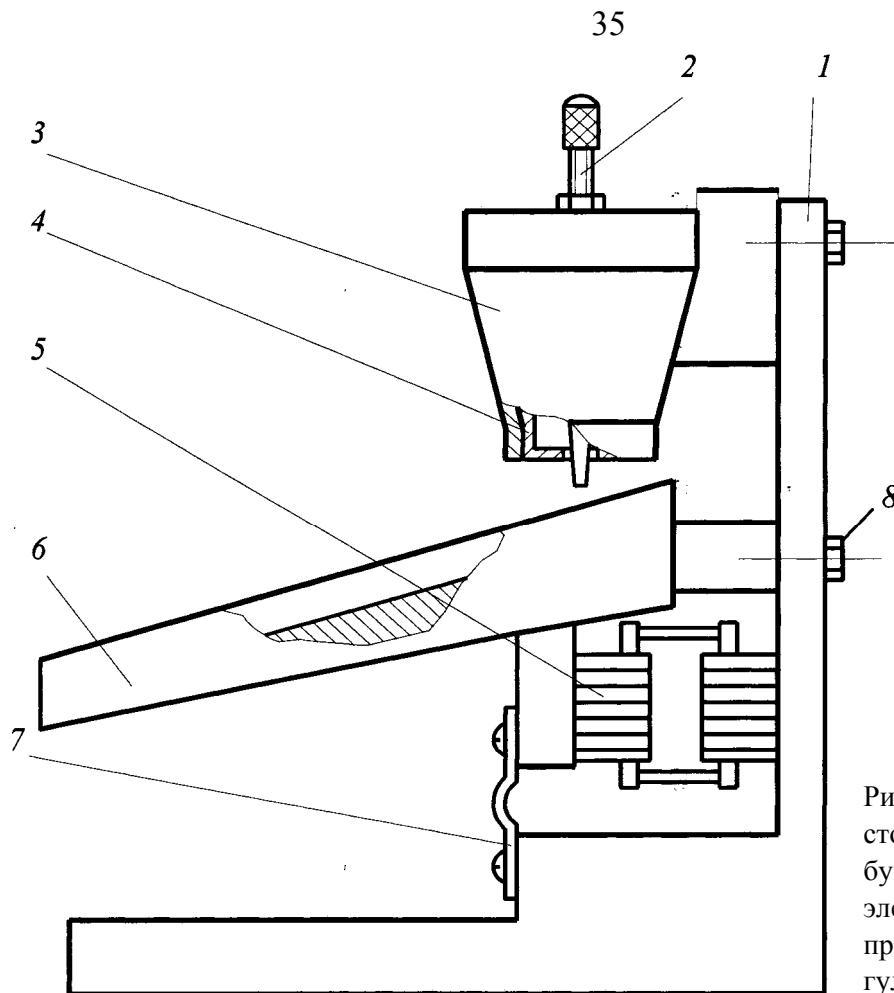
Схема дозатора: 1 - стойка; 2 - стержень; 3 - бункер; 4 - фильера; 5 - электромагнит; 6 - лоток; 7 - пружина; 8 - регулировочный винт
